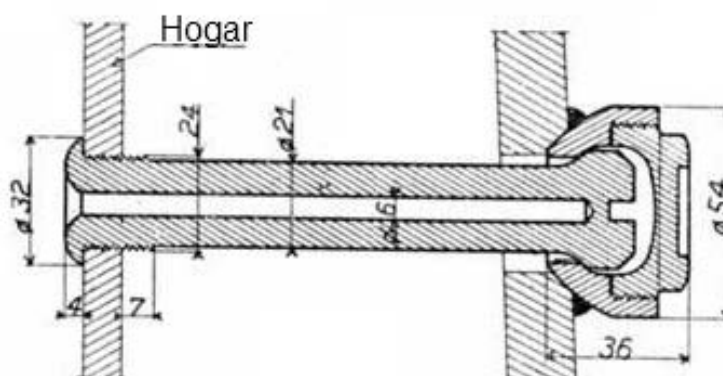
Virotillo con cabeza articulada y asiento soldado
